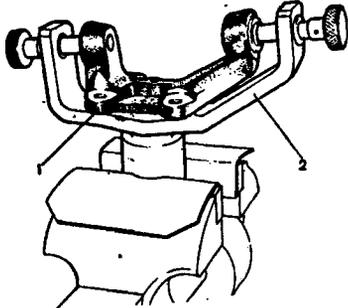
Проверка поворотного кулака: 1 - поворотный кулак; 2 - калибр А.96008
